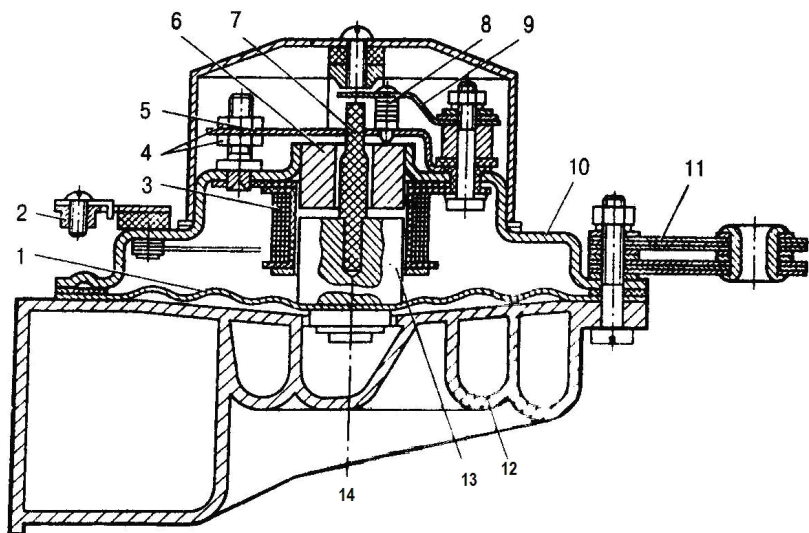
Тональный рупорный сигнал: 1 – мембрана; 2 – вывод обмотки; 3 – обмотка электромагнита; 4 – регулировочные гайки; 5 – пластина неподвижного контакта; 6 – сердечник электромагнита; 7 – упорный штифт; 8 – контакты; 9 – пружина подвижного контакта; 10 – корпус; 11 – кронштейн; 12 – рупор; 13 – яркорь
